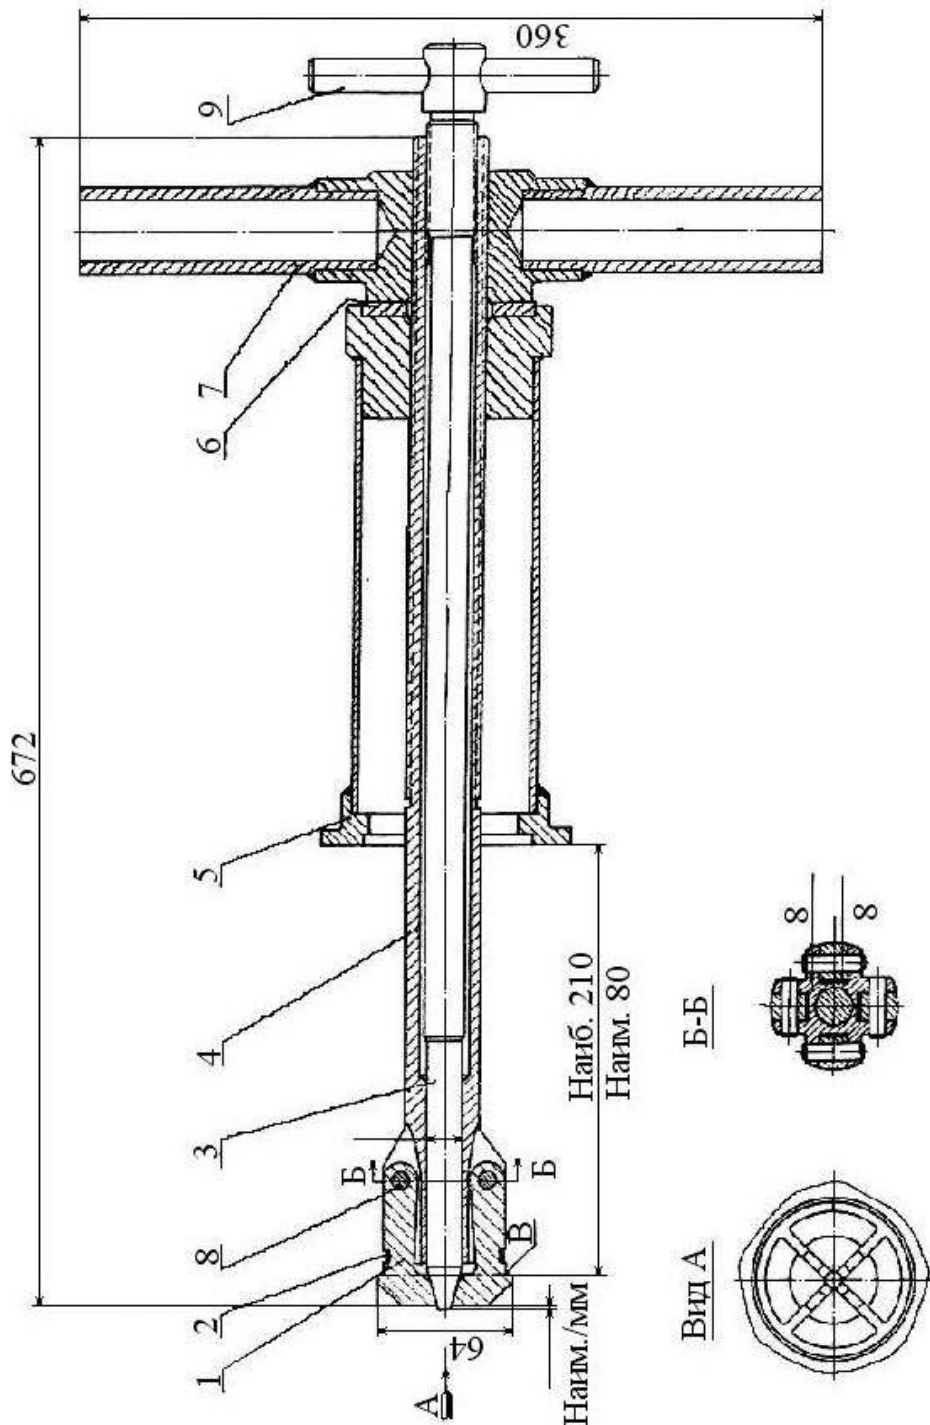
Приспособление для выпрессовки глубокоседающих тонкостенных втулок СД 7110 – 0001/00 – 000
